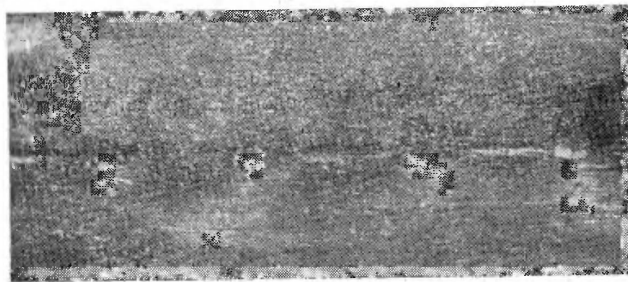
Сварной шов трубы из алюминия АД1, полученный при пульсации сварочного тока с частотой  $f = 150$  Гц
